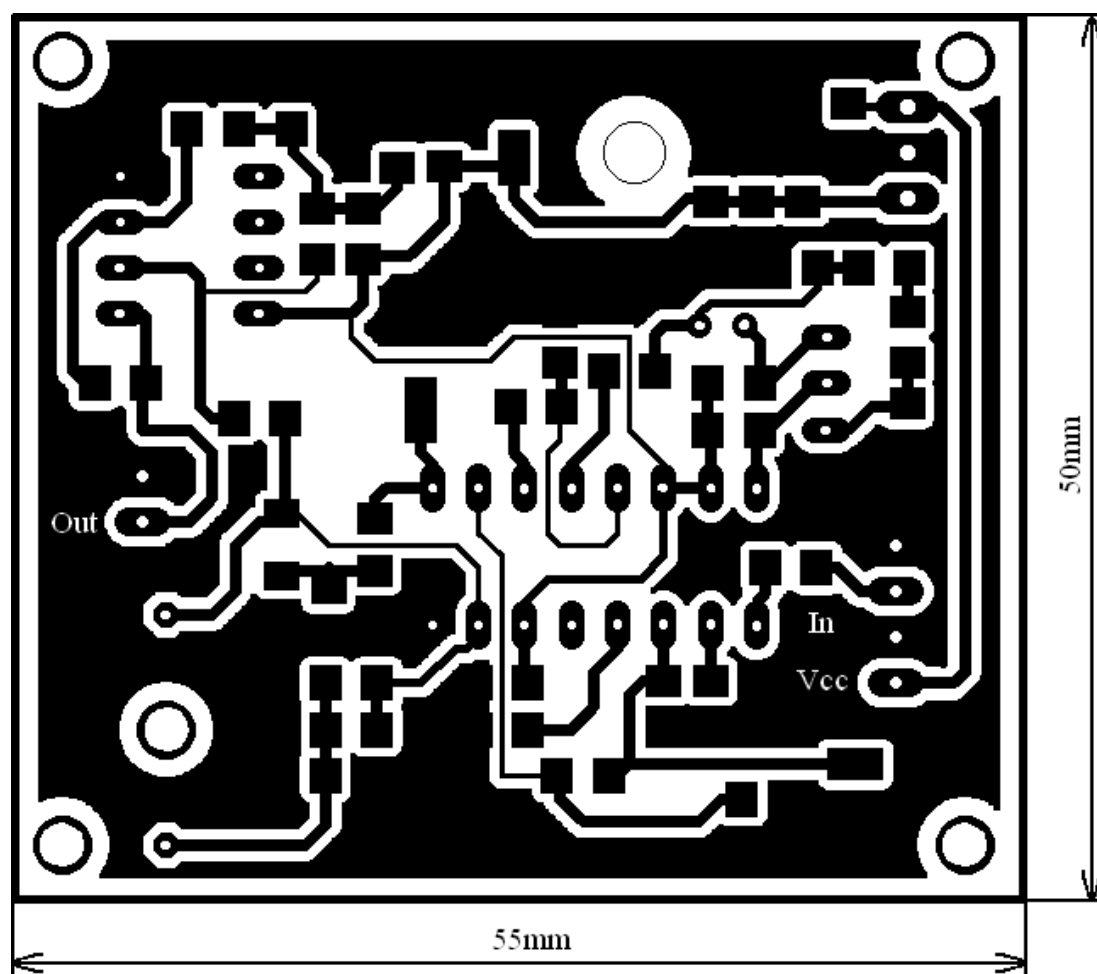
Rozmístění součástek předzesilovače, horní pohled
